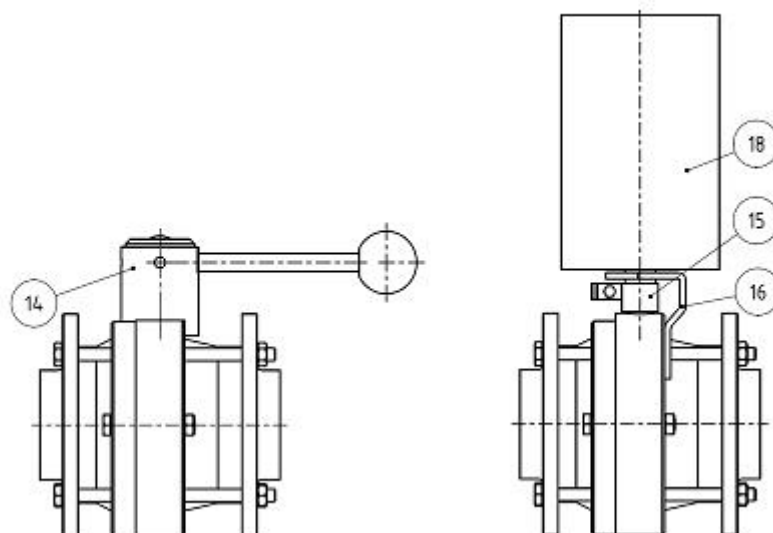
Kugelventil-ZF mit Handbetätigung oder pneumatischem Antrieb
